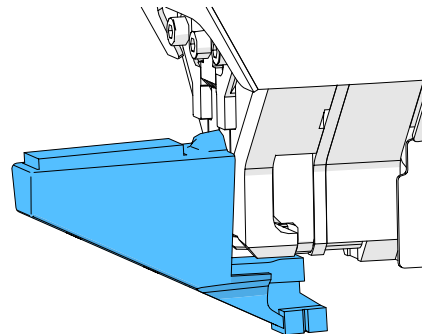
Ajutor pentru configurare Aliniere orizontală
